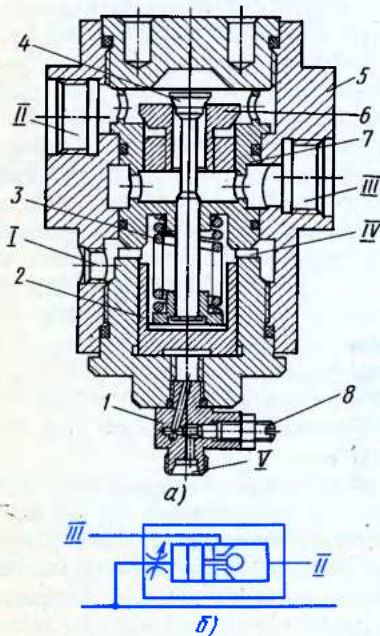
Тормозной клапан с запорно-регулирующим элементом седельного типа крана КС-3562Б (а) и его обозначение на схемах (б): 1 — демпфер, 2 — поршень, 3 — пружина, 4, 6 — клапаны, 5 — корпус, 7 — седло, 8 — игла демпфера
